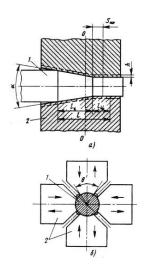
Инструмент и заготовка при ротационной ковке: а - сечение в направления продольной оси заготовки; б - поперечное сечение; 1 - заготовка; 2 - бойки; I - область пластической деформации; /ц - калибрующий участок; h - радиальное обжатие; в - рабочий участок бойка
